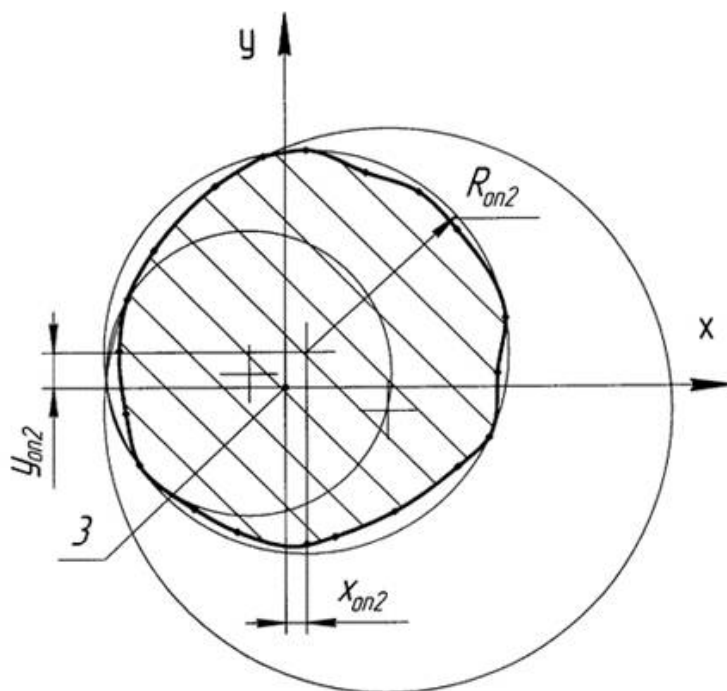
Схема визначення описаного кола перетину базової поверхні деталі
